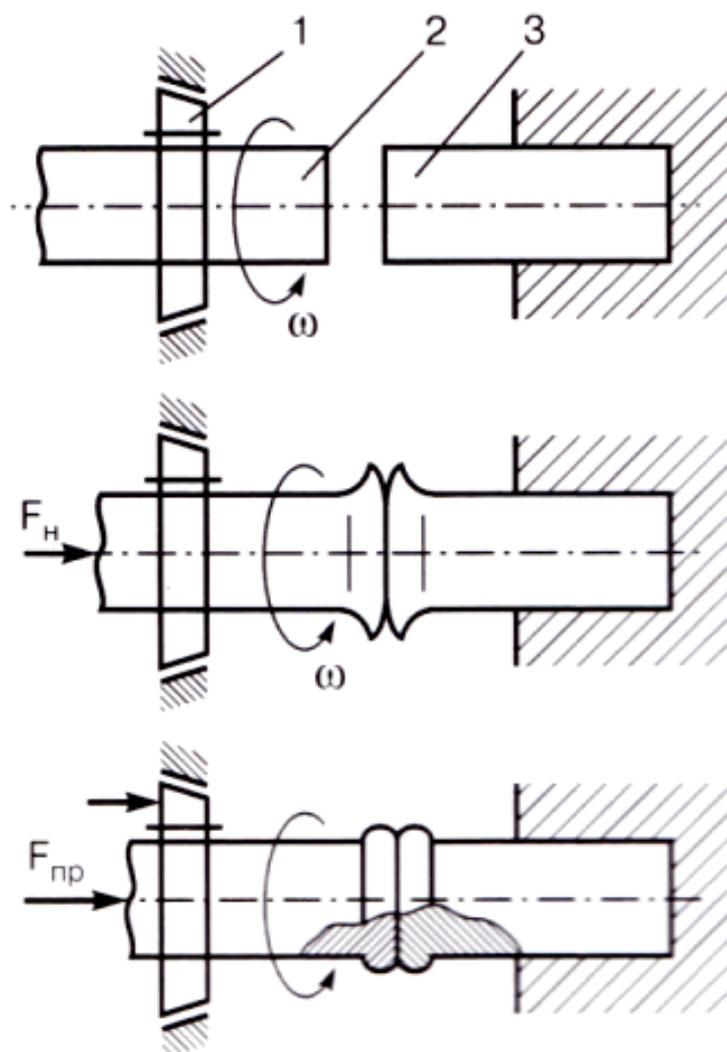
Схема конвенциональной сварки трением с непрерывным приводом:
